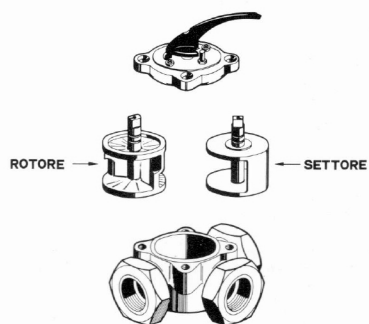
Esplosione valvola a 3 vie con interno a rotore o settore.
